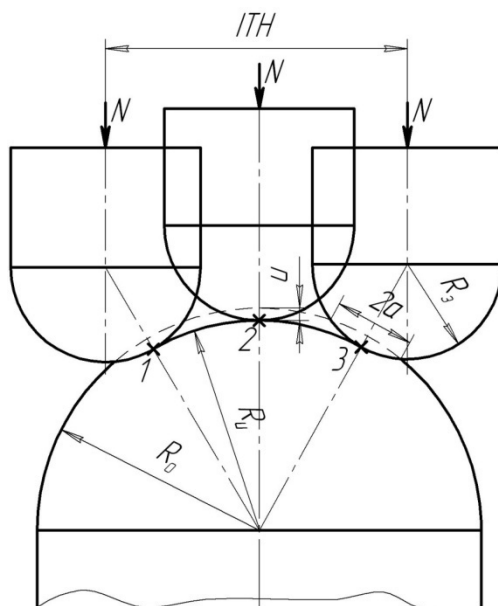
Контакт сферической заготовки со сферической поверхностью установочной опоры
